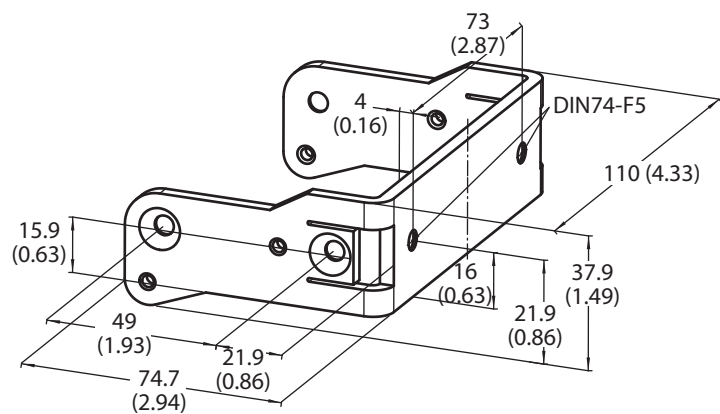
Esquema de dimensiones, juego de montaje 2 442L-AMBSZMN2
